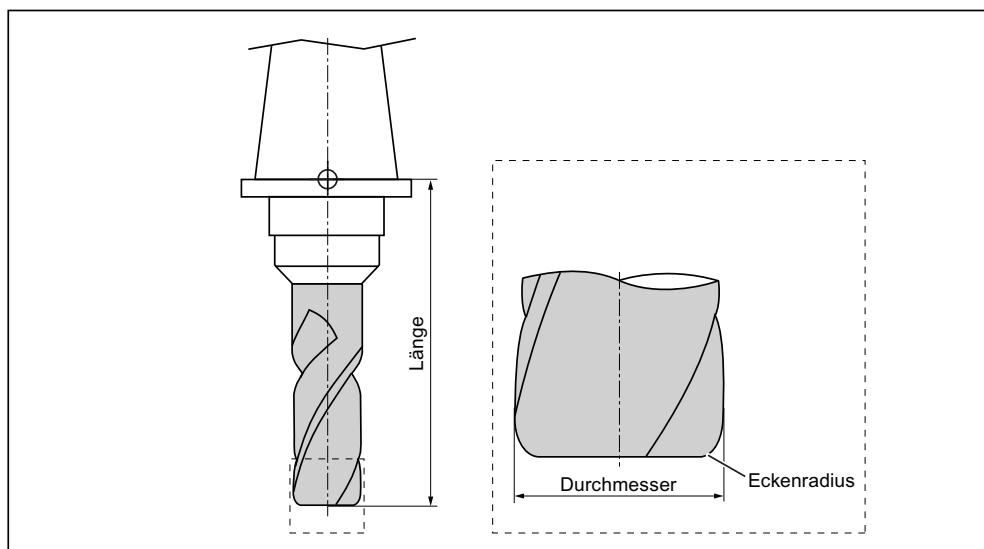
3D-Werkzeug am Beispiel eines Schaftfräsers mit Eckenverrundung (Typ 121)
